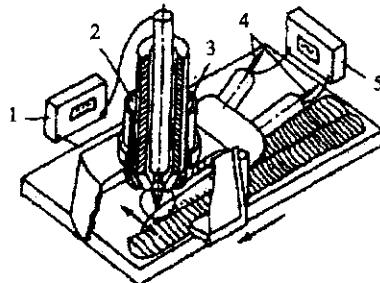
Схема устройства для плазменной наплавки горячей проволокой:
